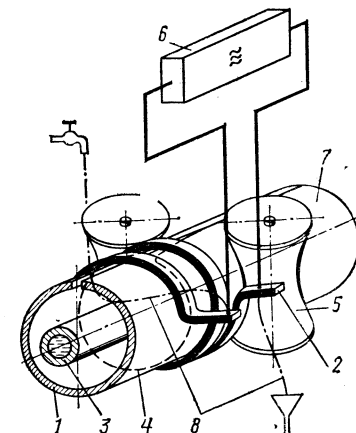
Сварка токами высокой частоты кольцевым индуктором (метод «Induweld»):
